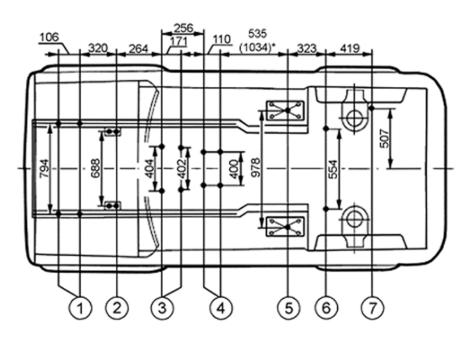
Точки крепления двигателя и подвесок на кузове 21214, 2131:
